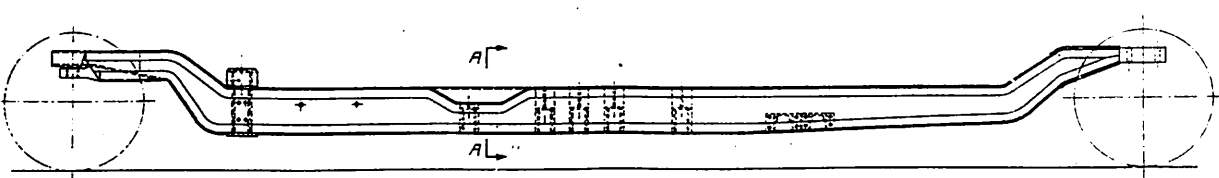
Genietetes Motortragrahmen für eine 150 PS dieselmechanische Maschinenanlage.
